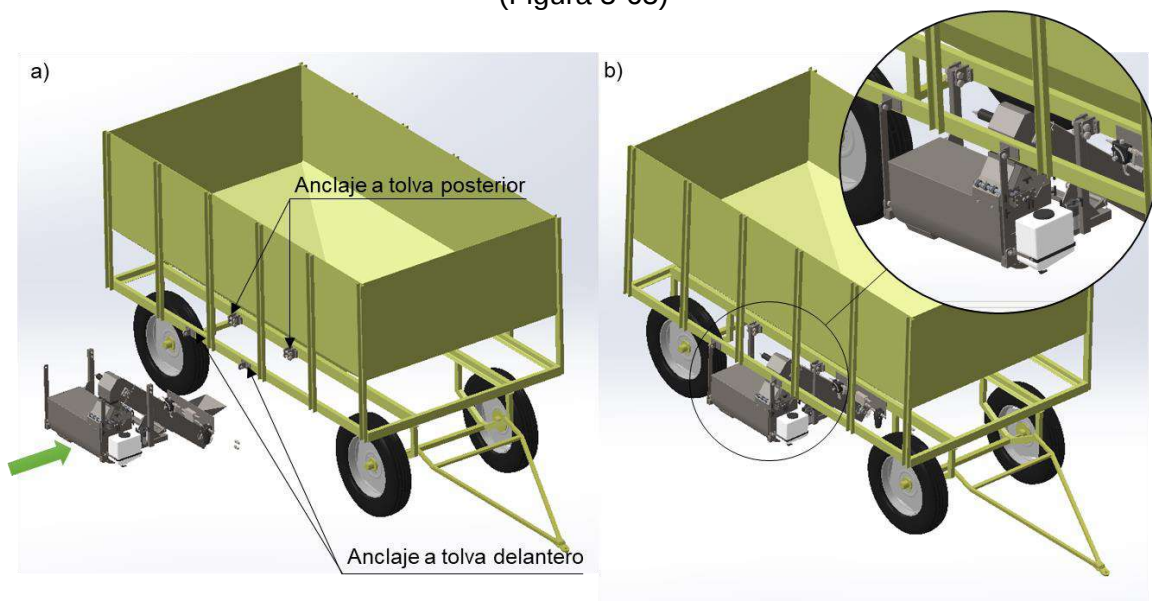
a) Montaje de anclajes a chasis de tolva. b) Dispositivo montado en tolva.
